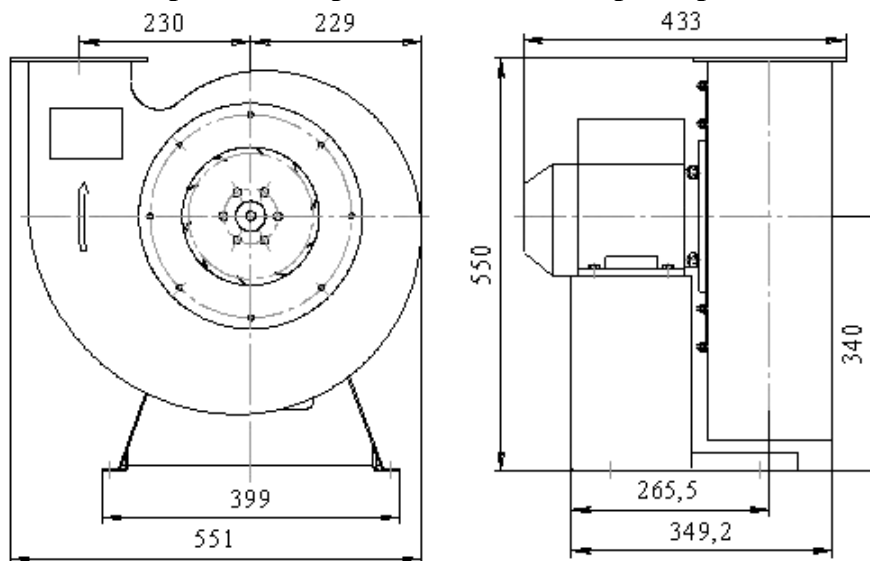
Вентиляторы ВРП-100-45-3,15. Габаритные размеры
